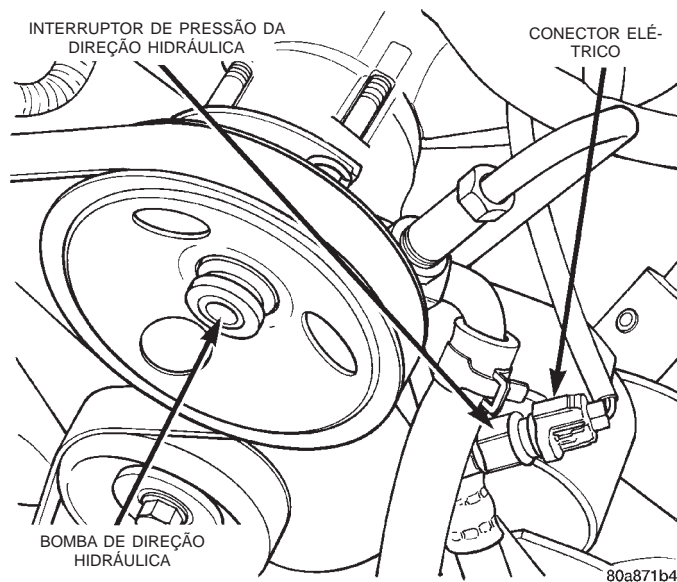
Interruptor de Pressão da Bomba de Direção Hidráulica—Motor 2.5L
